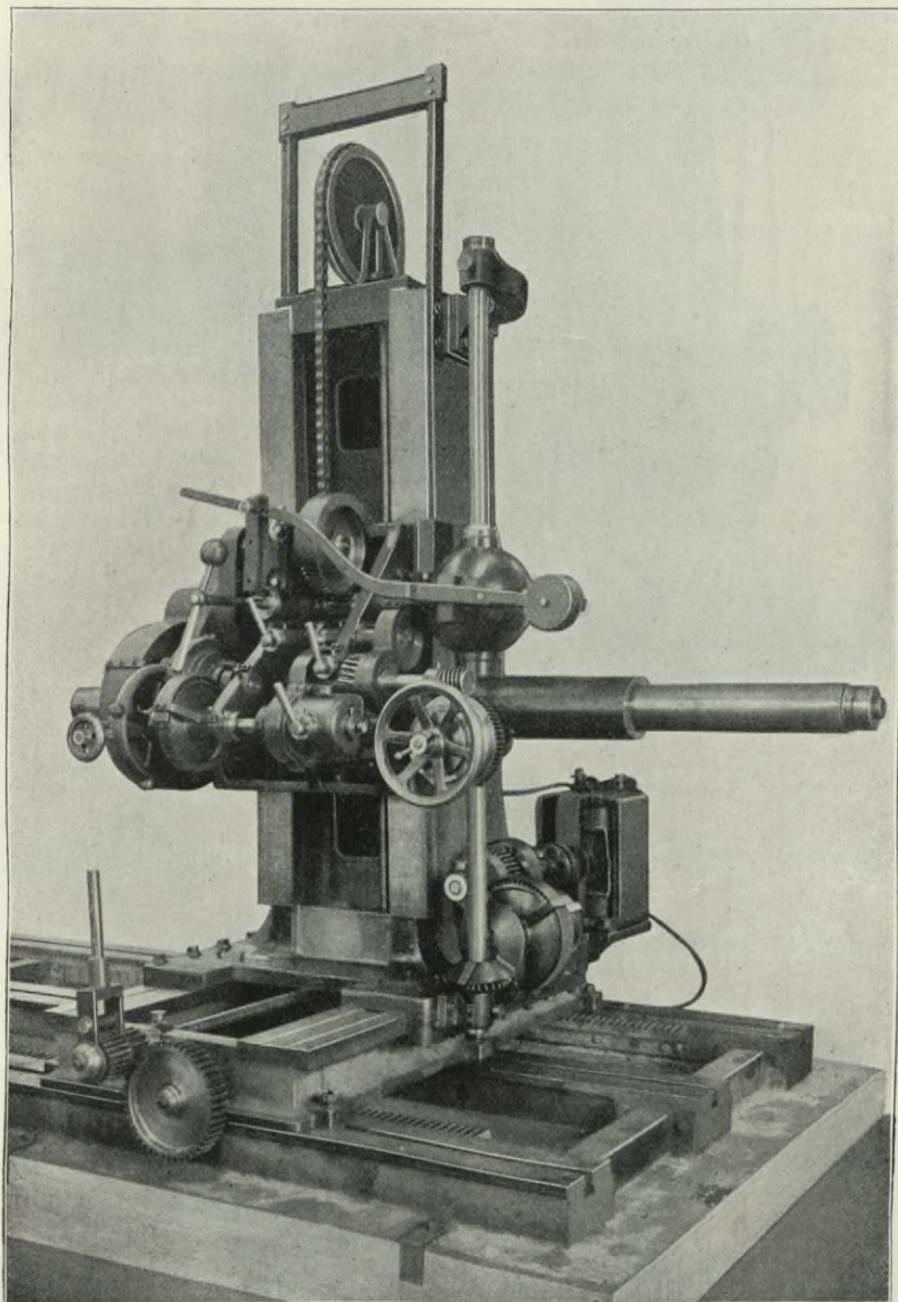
Düsseldorfer Werkzeugmaschinenfabrik Habersang & Zinzen.
